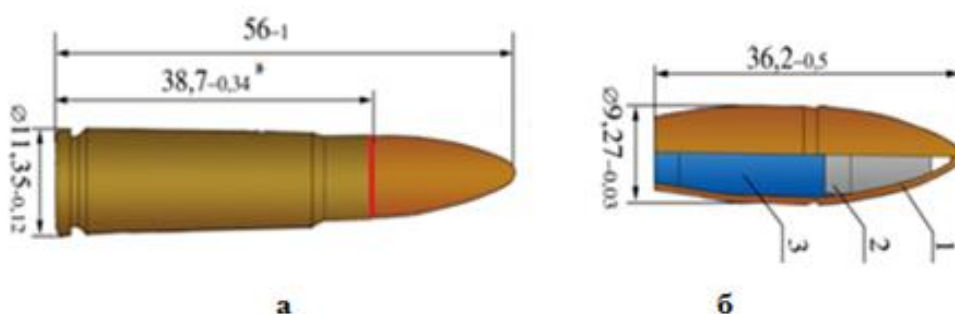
9-мм патрон СП5 с бронебойной пулей: а – патрон; б – пуля; 1 – оболочка; 2 – рубашка свинцовая; 3 – сердечник;
